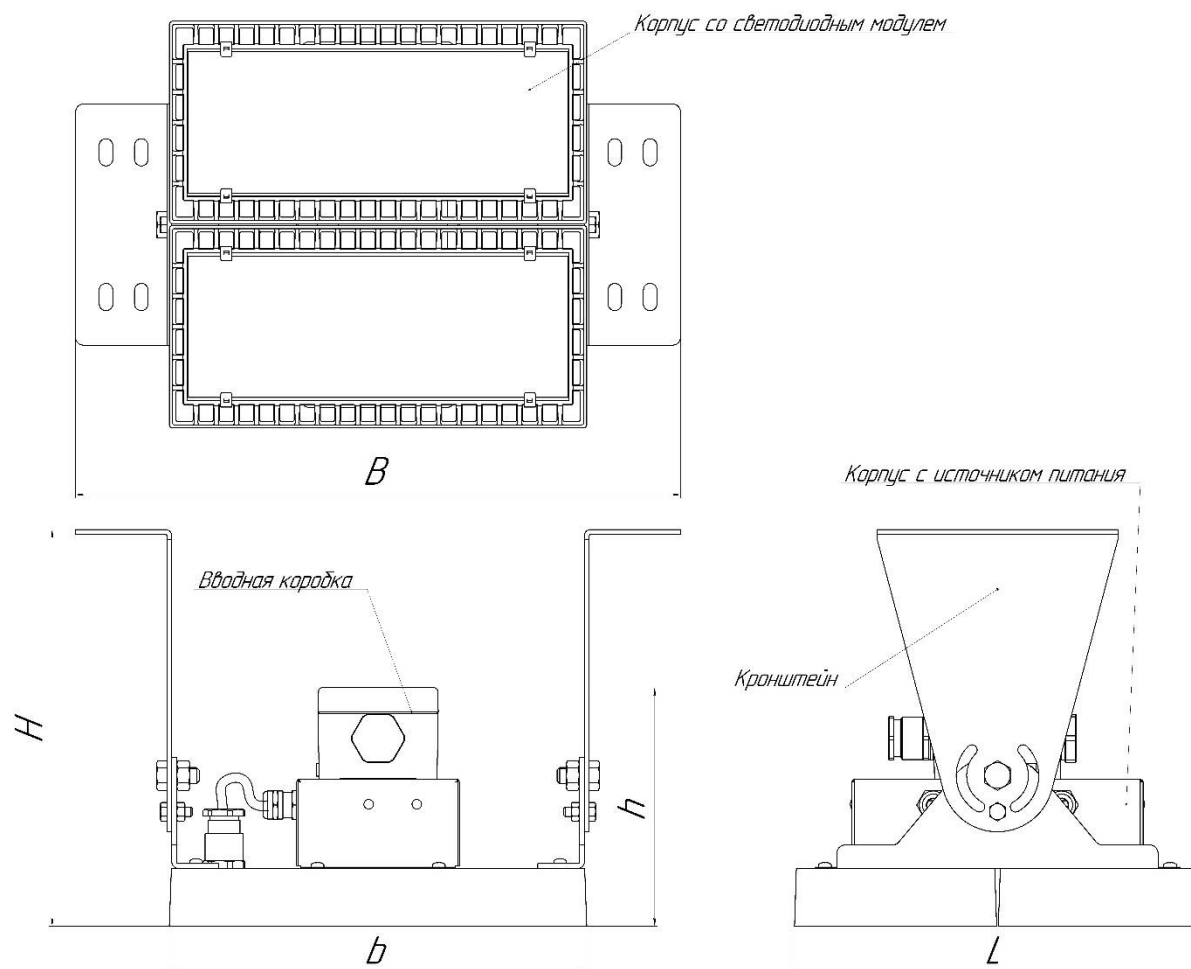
а - Габаритные размеры светильника ДСП36-110, 160, 210, 270
